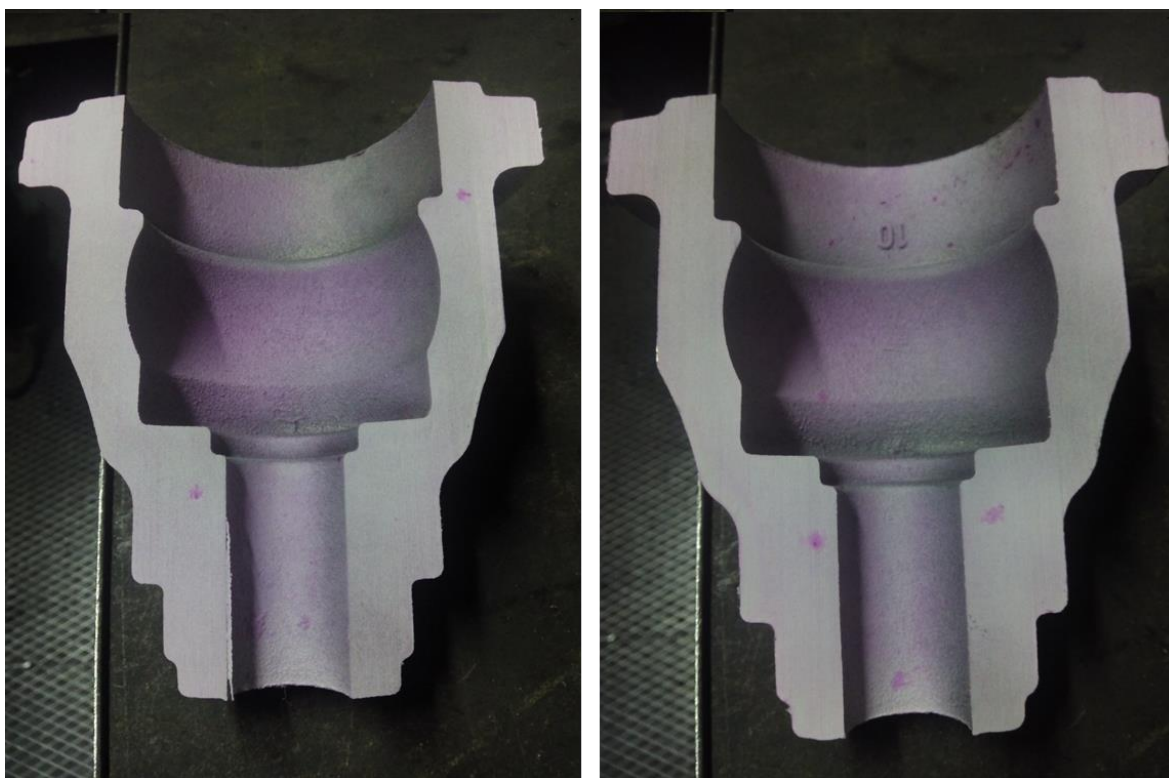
Foto da peça 2, cortada segundo o plano de separação, depois do ensaio de Líquidos Penetrantes.
